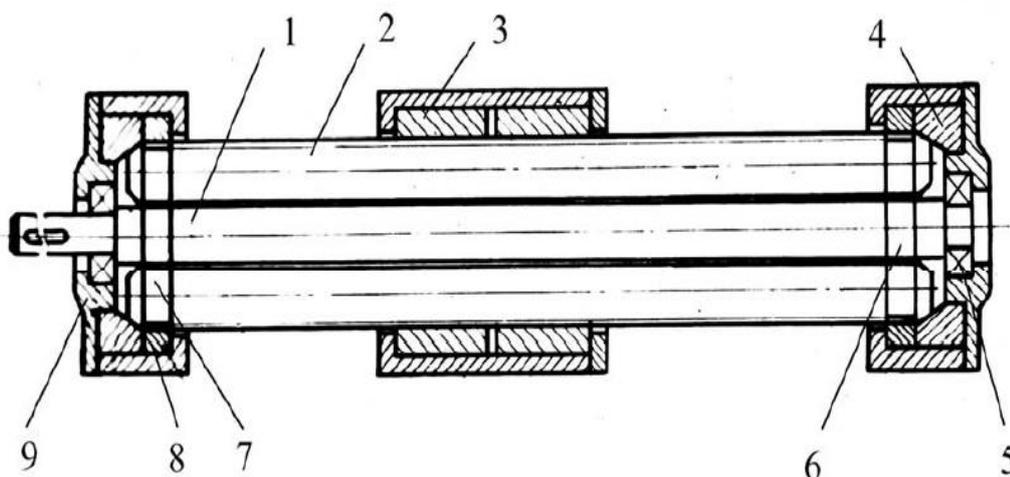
Передача с длинными резьбовыми роликами и опорными гайками
